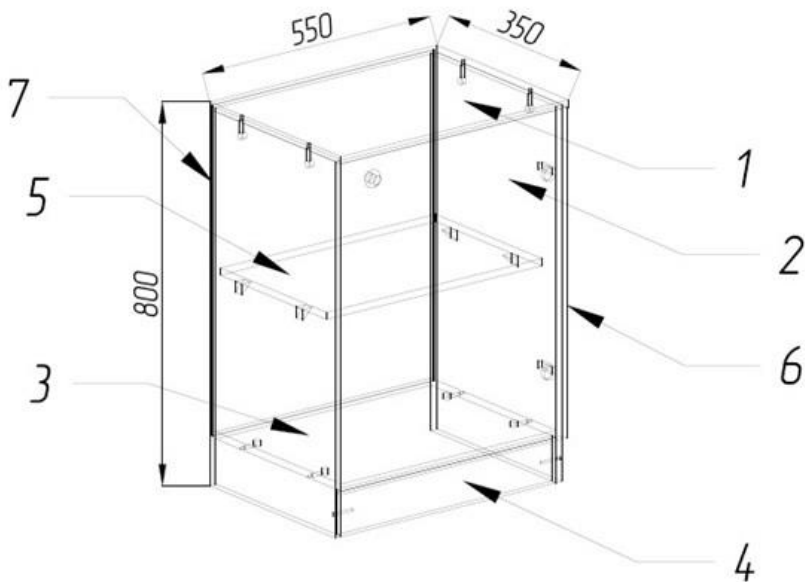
Конструкція: 1 - кришка; 2 - бічні стінки; 3 – горизонтальний щит; 4 - цоколь; 5 - полиця; 6 - дверцята; 7 - задня стінка
